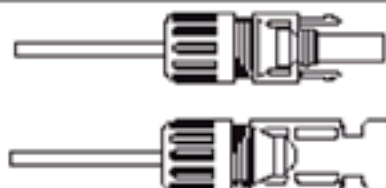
Stecker mit aufgeschraubter Überwurfmutter
